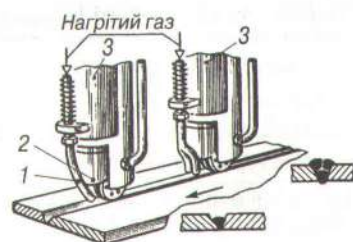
Загальний вигляд механізованого зварювального вузла і зварювальної головки:
